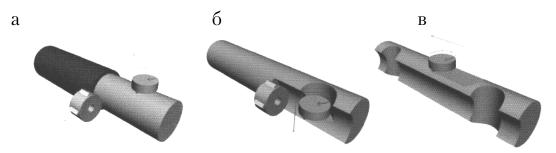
Способы формирования поверхности обрабатываемого бревна: а – цилиндрование; б – выборка монтажного паза; в – выборка венцовых чашек
